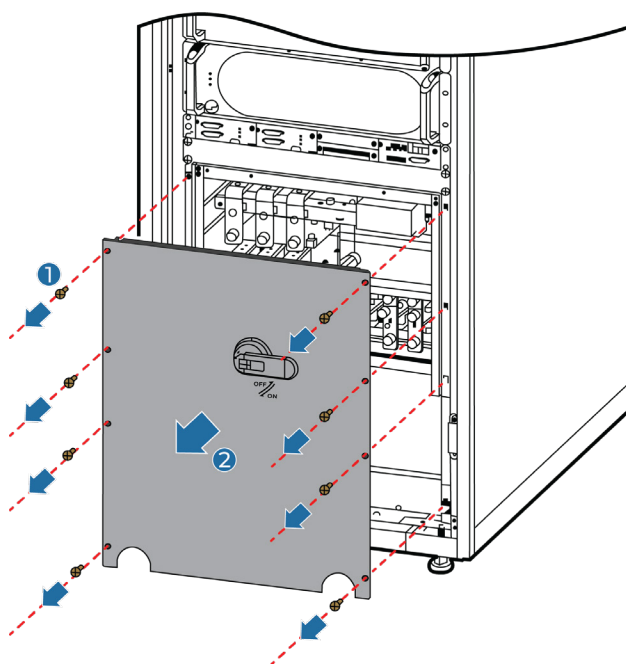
EXTRACCIÓN DE LA CUBIERTA
